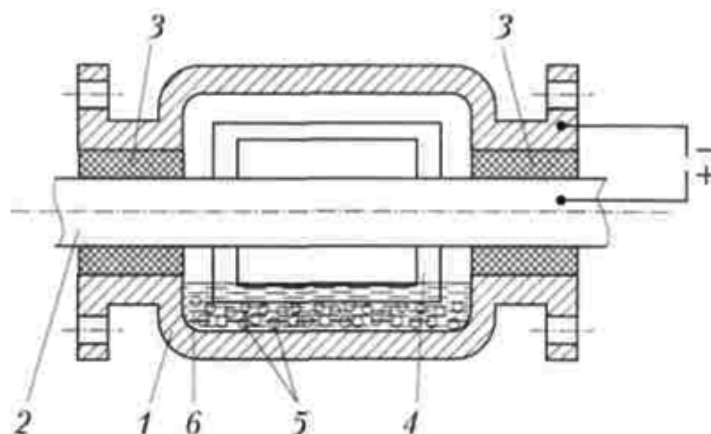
Схема рабочей части станка для обработки внутренней поверхности корпуса компрессора
